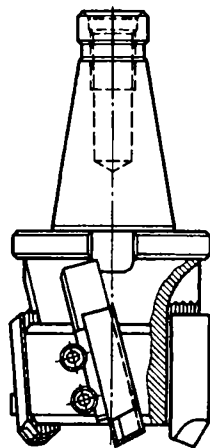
Сборная торцовая фреза со вставными ножами
